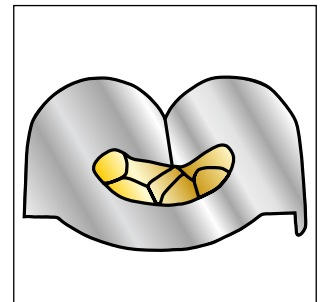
Kontakt mit kleinem Headroom, schlecht platziert im Werkzeug
